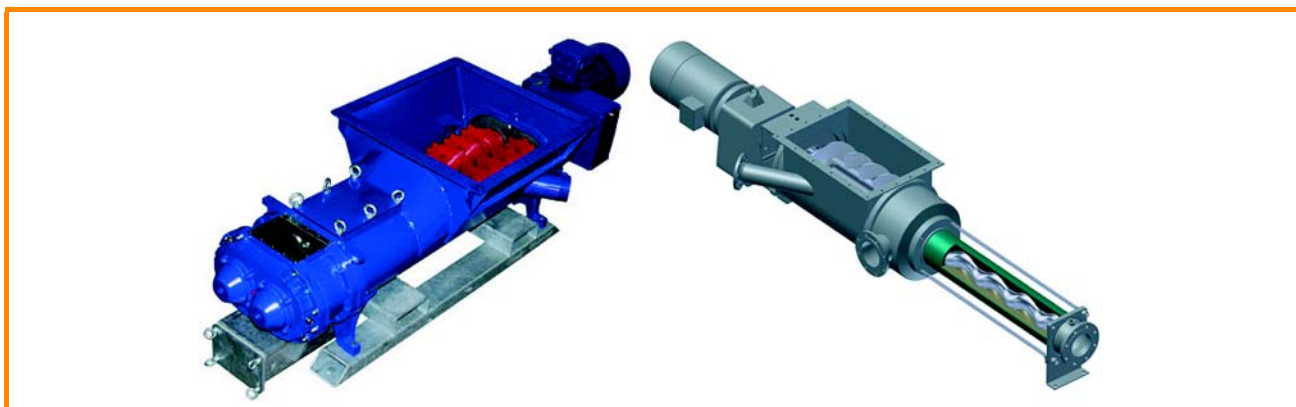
Las bombas de tolva con bombas de desplazamiento rotatorio integrado (izquierda) y bomba de tornillo de rotor único excéntrico (derecha) [Hugo Vogelsang Maschinenbau GmbH (izquierda), Netzsch Mohnopumpen GmbH]
